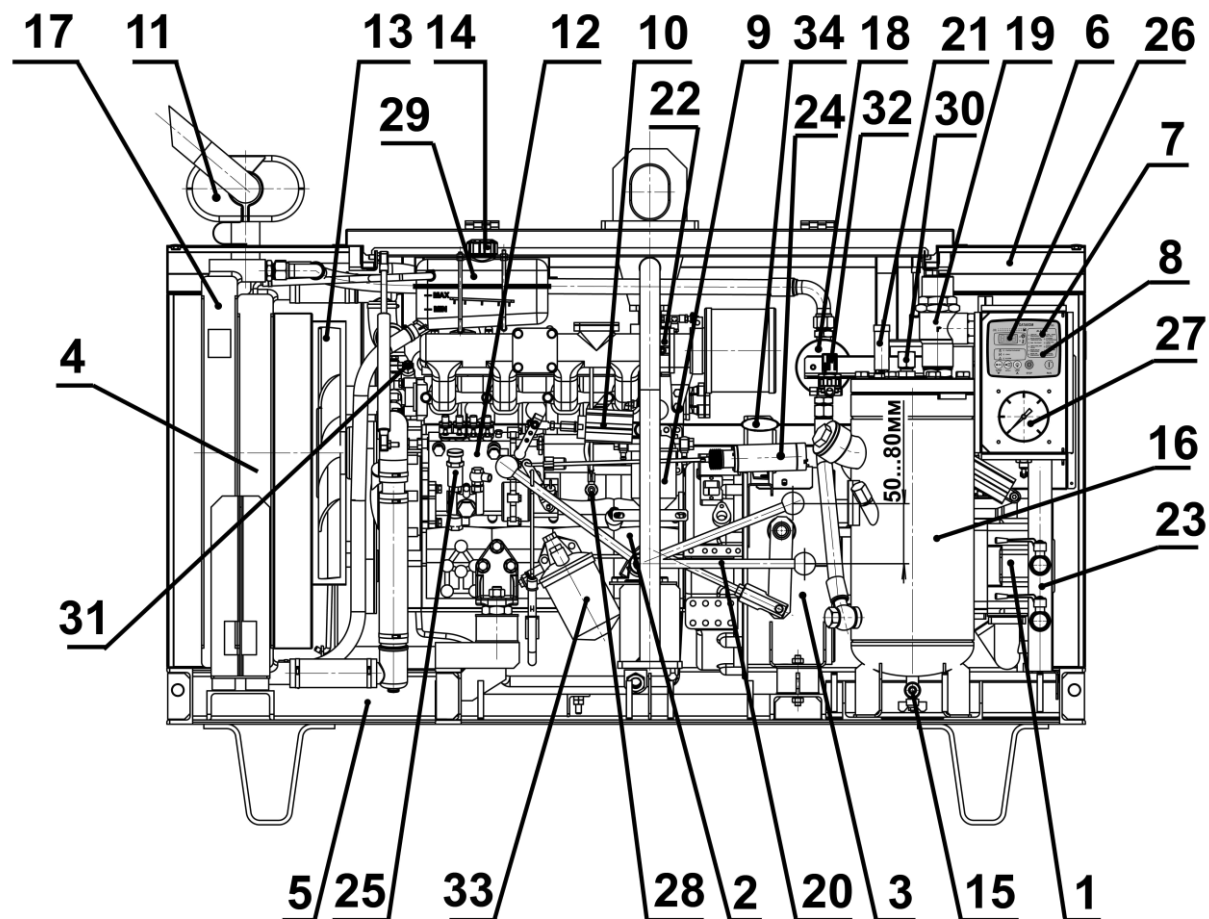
Габаритный чертеж станции компрессорной ЗИФ-ПВ3,5/0,7F (АРМ9-33).
